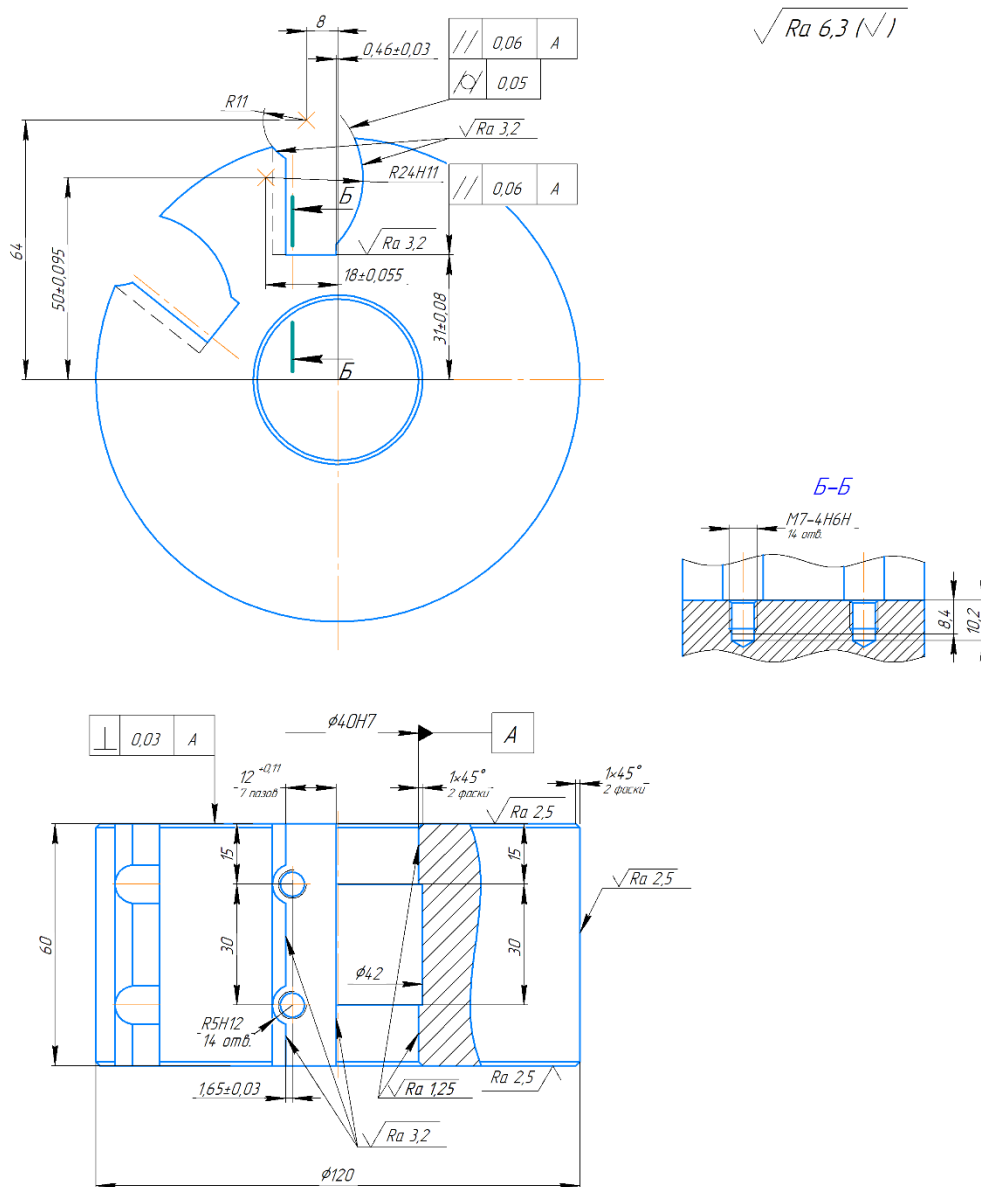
Чертеж корпуса дереворежущей цилиндрической сборной фрезы
